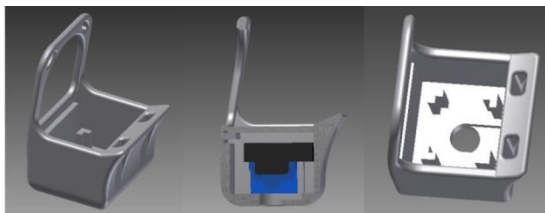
Сборка корпуса в САПР Autodesk Inventor
